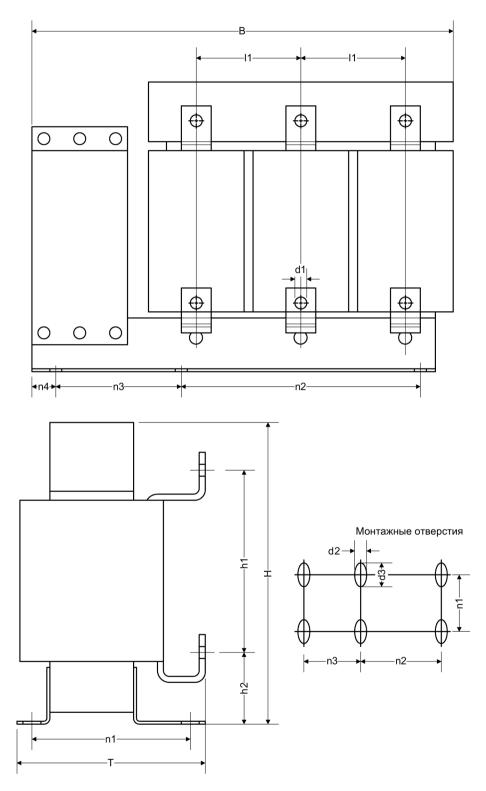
Габаритный чертеж синусоидального фильтра
